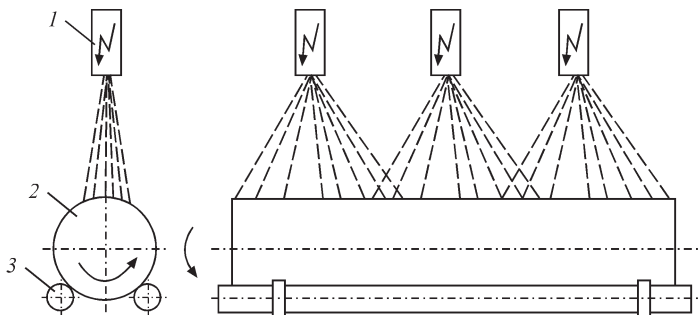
Схема оплавлення зливка: 1 — електронно-променева гармата; 2 — зливоч; 3 — валки
